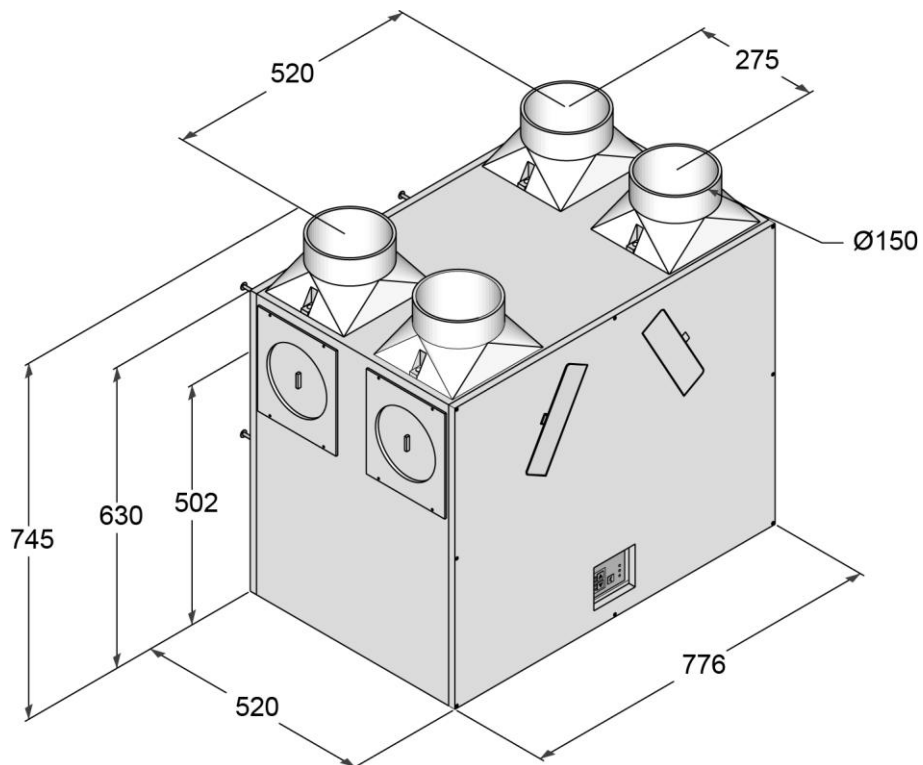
SEVi ZG400; Abmessungen Maßangaben in Millimeter
